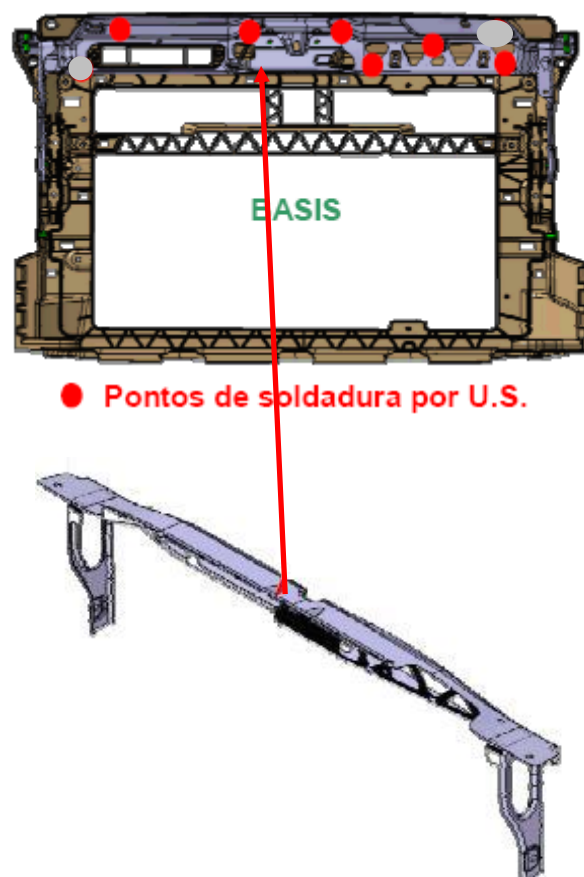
Montagem da chapa em todos os “Frontends”, fixação por pontos de soldadura por Ultra-Sons
